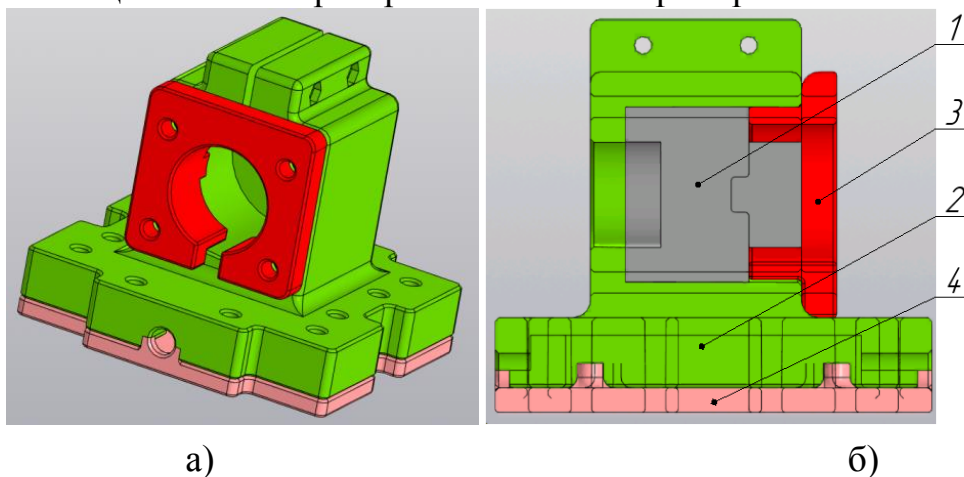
Технологическое приспособление в сборе: а – общий вид; б – вид в разрезе
